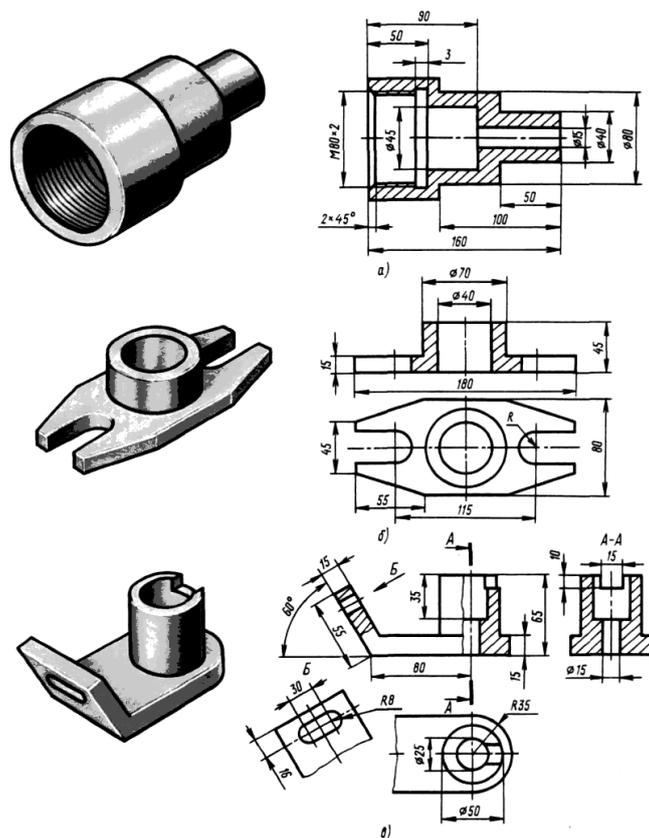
Пример выполнения рабочих чертежей деталей
